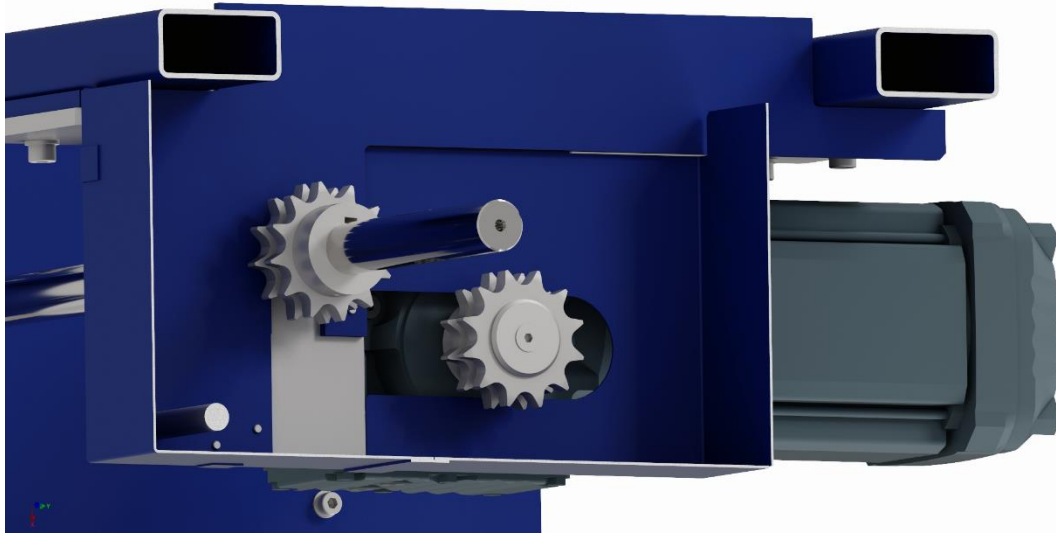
Pohled řezem do prostoru řetězu v pohonné jednotce [Autor]
